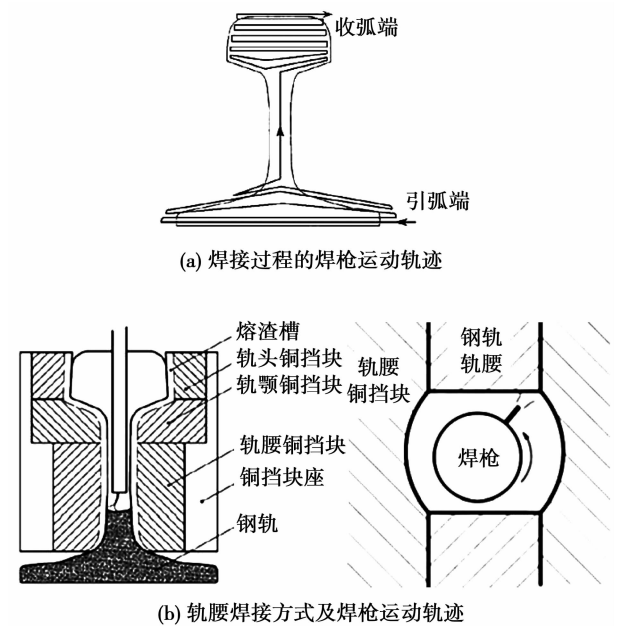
钢轨窄间隙电弧焊接过程的焊枪运动轨迹
